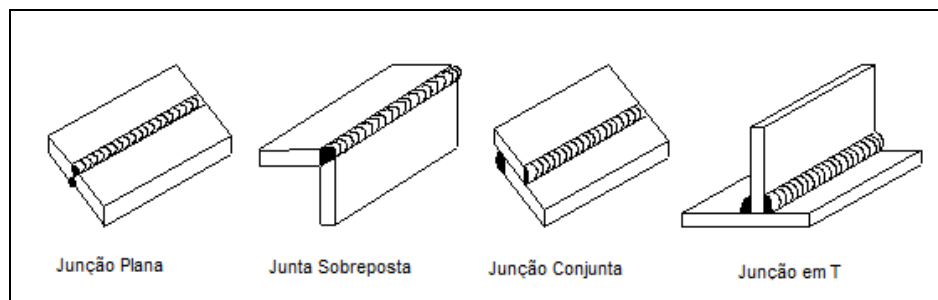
Tipos de junta na soldagem eletrodo revestido
